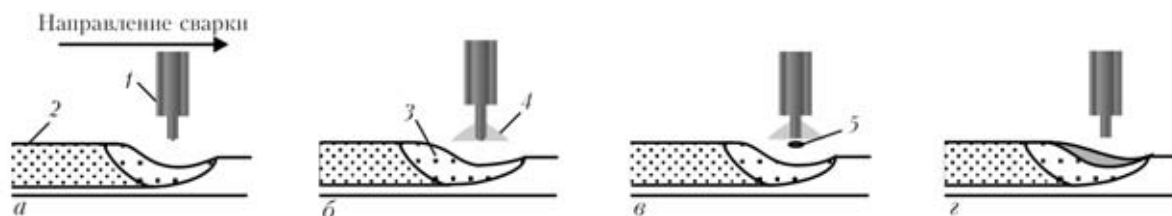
Схема модели процесса сварки МАГ: 1 — электродная проволока; 2 — металл шва; 3 — расплавленная ванна; 4 — дуга; 5 — перенос металла
